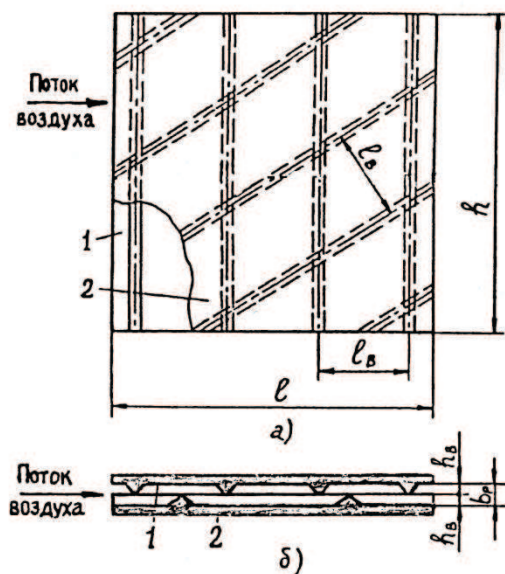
Схема формирования воздушного канала между попарно сложенными пластинами мипласта: а – вид сбоку; б – вид сверху; 1 – поток воздуха; 2 – пластина с вертикально расположенными выступами; 3 – пластина с наклонёнными выступами навстречу потоку воздуха
